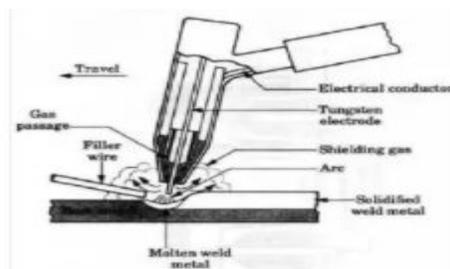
proceso de soldadura tipo GTAW (([DOC](#)) [SOLDADURA PARA EL MANTENIMIENTO "](#)
